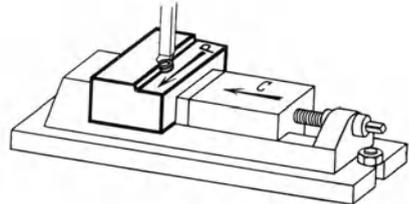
Aufnahme der Schnittkraft beim Spannen. P Schnittdruck, C Spanndruck.
